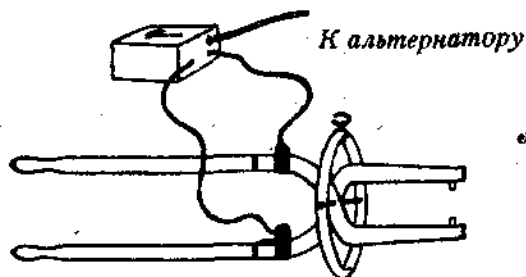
Переносный аппарат для точечной сварки.
